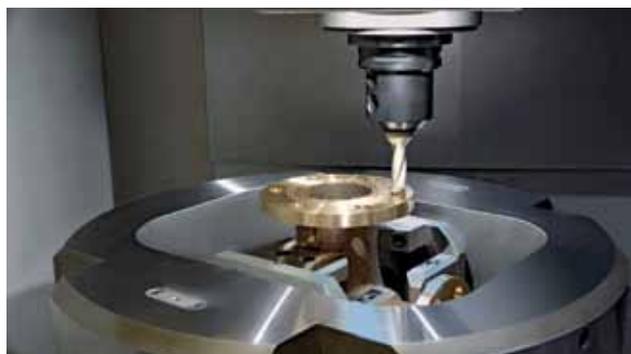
Станок оснащен полноценным фрезерным шпинделем, на котором устанавливаются приводные инструменты для сверления и фрезерования
